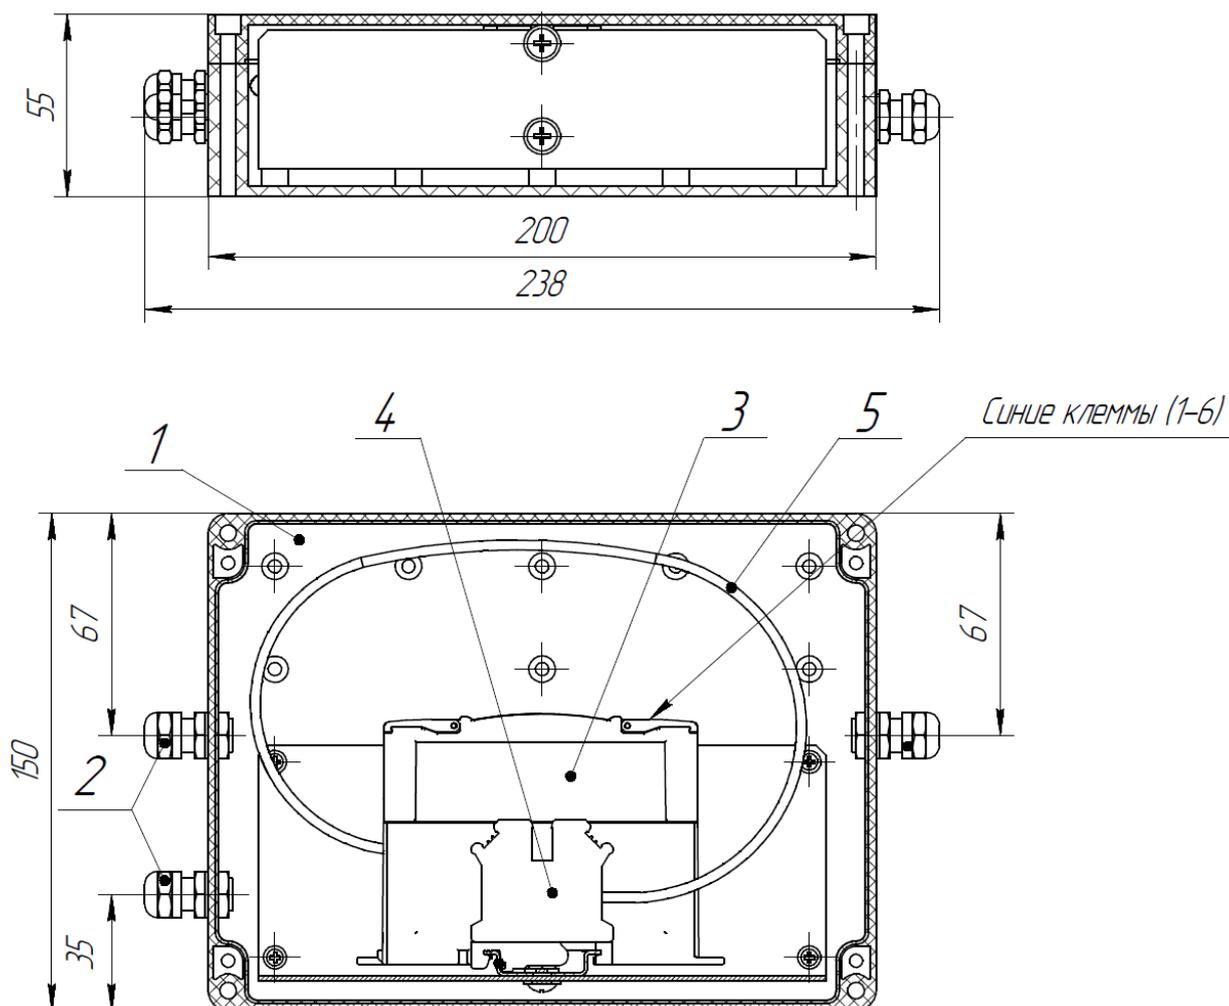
Внешний вид барьерной коробки БК-1 исп. ТП
